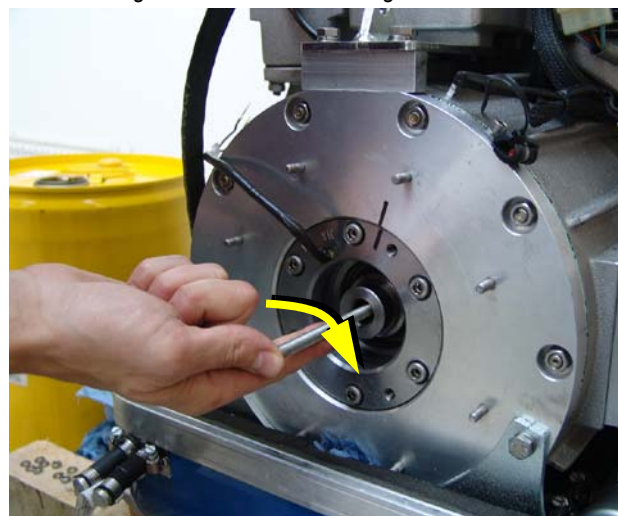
Befestigungsschrauben anziehen
